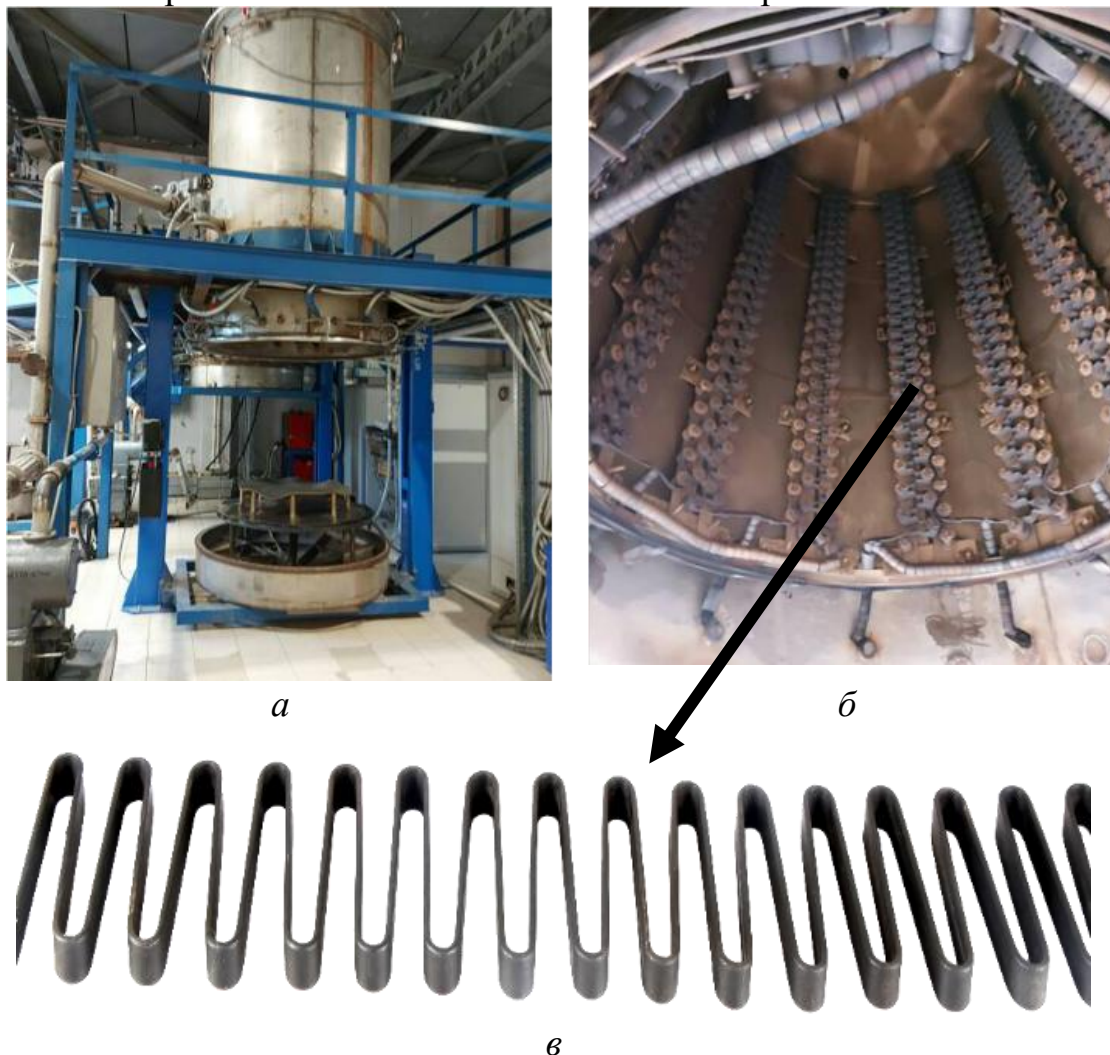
Промышленная вакуумная печь, используемая ООО «НПО «СПЛАВ-Ти» (а), внутренний вид колпака печи с нагревательными элементами (б) и внешний вид нагревателя из сплава X20H80 с алюминидным покрытием, полученным по разработанной технологии (в)
